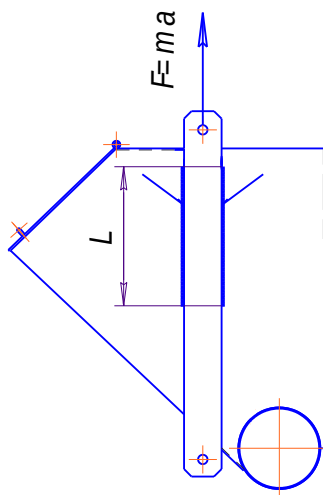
Схема сварного соединения пластины и бункера
